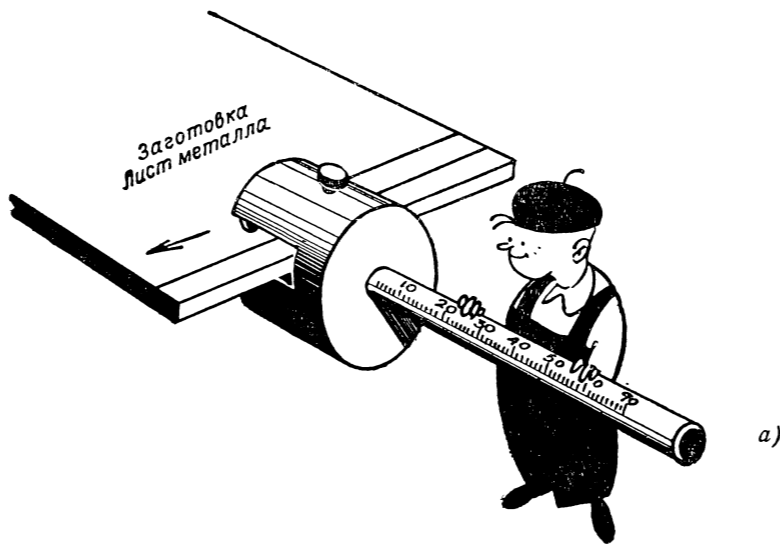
Приспособление для разметки полос: а — общий вид приспособления для разметки полос. Корпус. Линейка. Резец
